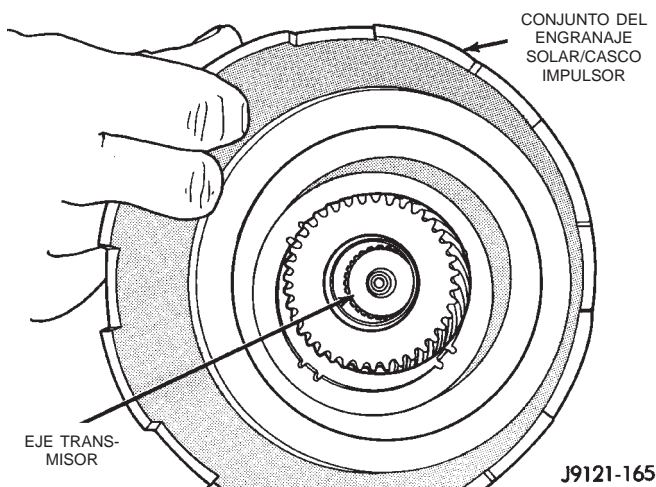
Instalación del engranaje solar y el casco impulsor ensamblados en el eje transmisor
